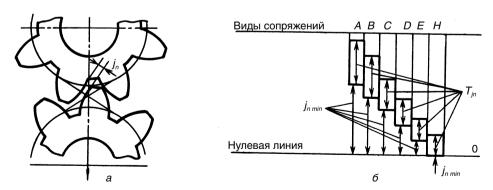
Сопряжение зубьев в зубчатой передаче: а — боковой зазор j_n , 6 — схема расположения полей допусков T_i , для принятых видов сопряжений
